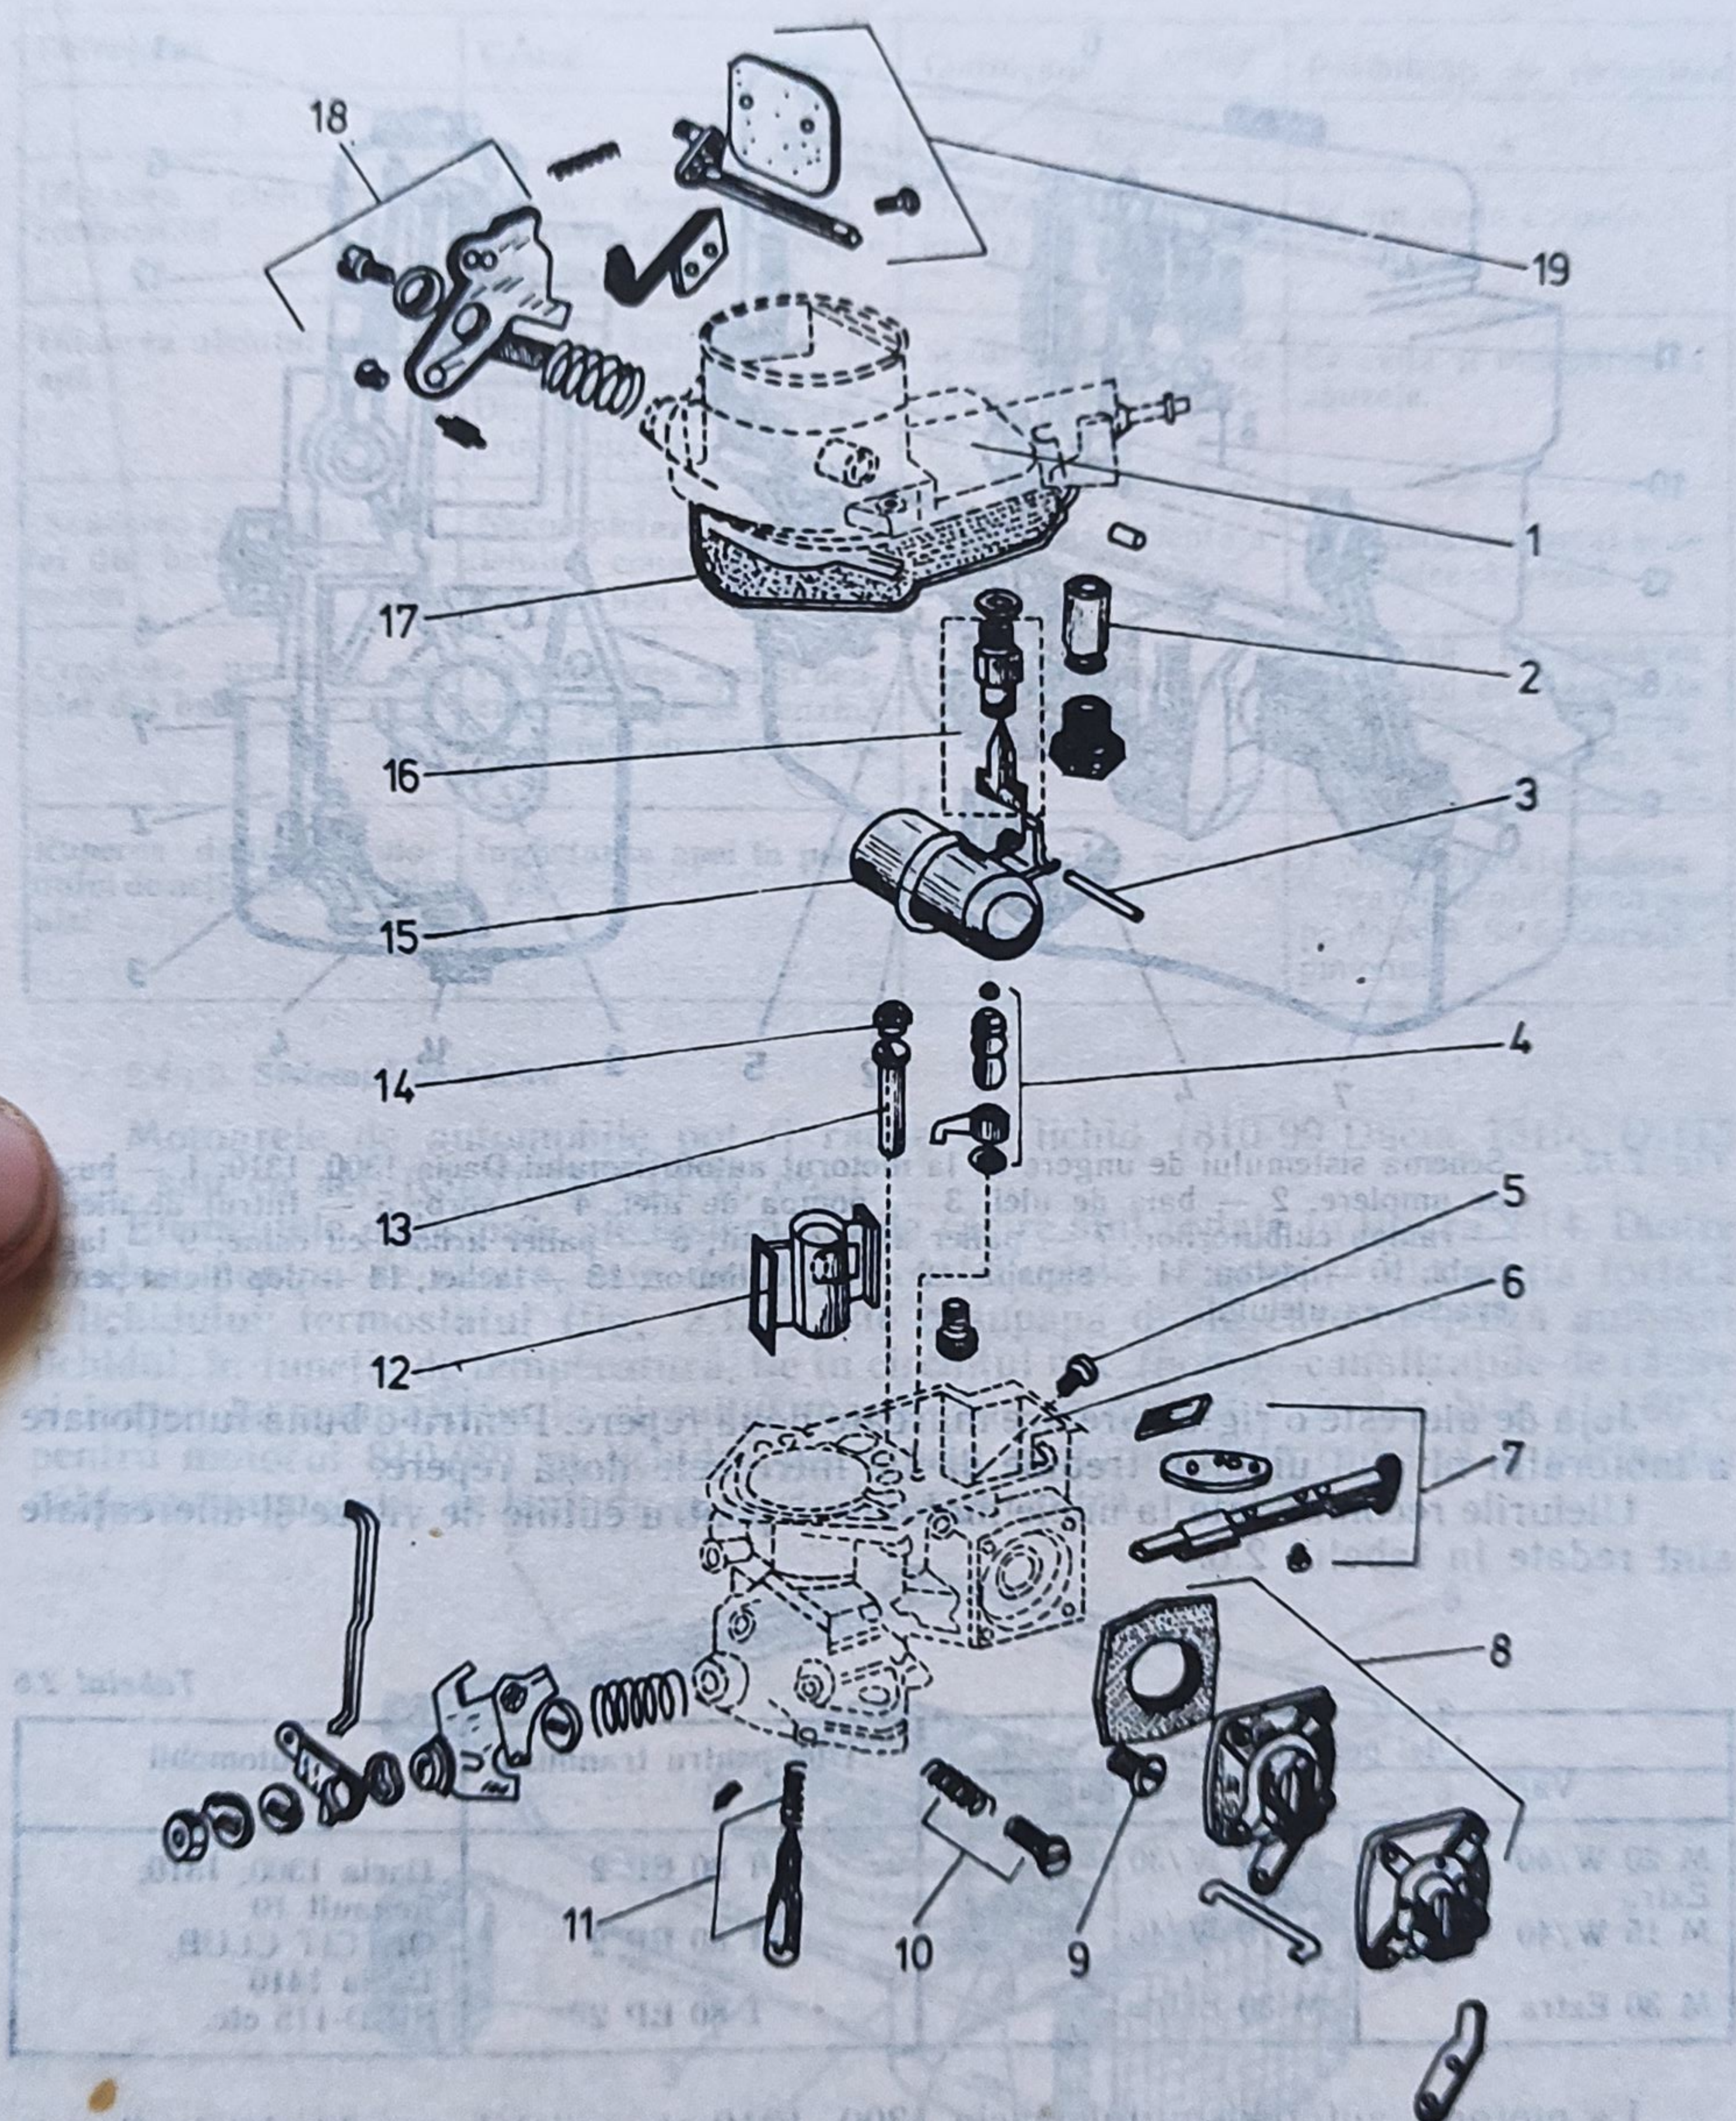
Carburatorul CARPIL 32 IRM WEBER: 1 — capac; 2 — filtru; 3 — știftul plutitorului; 4 — pulverizatorul cu supapă al pompei de accelerație; 5 — jiclor principal; 6 — capacul carburatorului; 7 — clapeta de accelerație; 8 — pompa de accelerație; 9 — jiclor de mers în gol; 10 — șurub cu arc pentru reglarea aerului la mers în gol; 11 — șurub pentru îmbogățire; 12 — concentrator; 13 — tub emulsor; 14 — jiclor compensator; 15 — plutitor; 16 — ansamblu cul-ventil; 17 — garnitura; 18 — dispozitiv de pornire la rece; 19 — clapeta de pornire.
